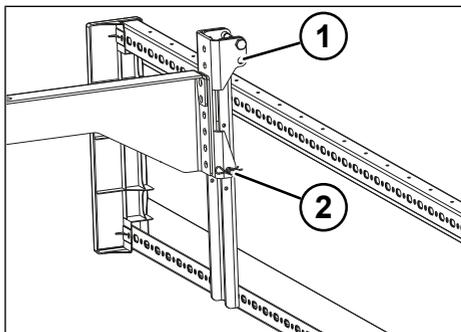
O dispositivo de proteção lateral está dobrado para baixo (vista da parte traseira)
